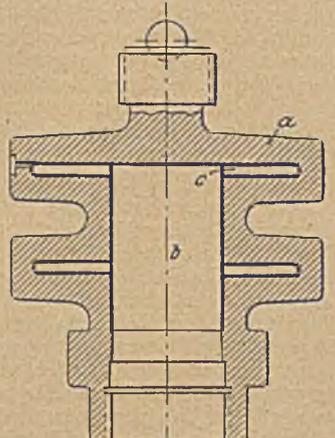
2-t-Hohlkörper Kraftprüfer für Zug und Druck mit Doppelkammern.
